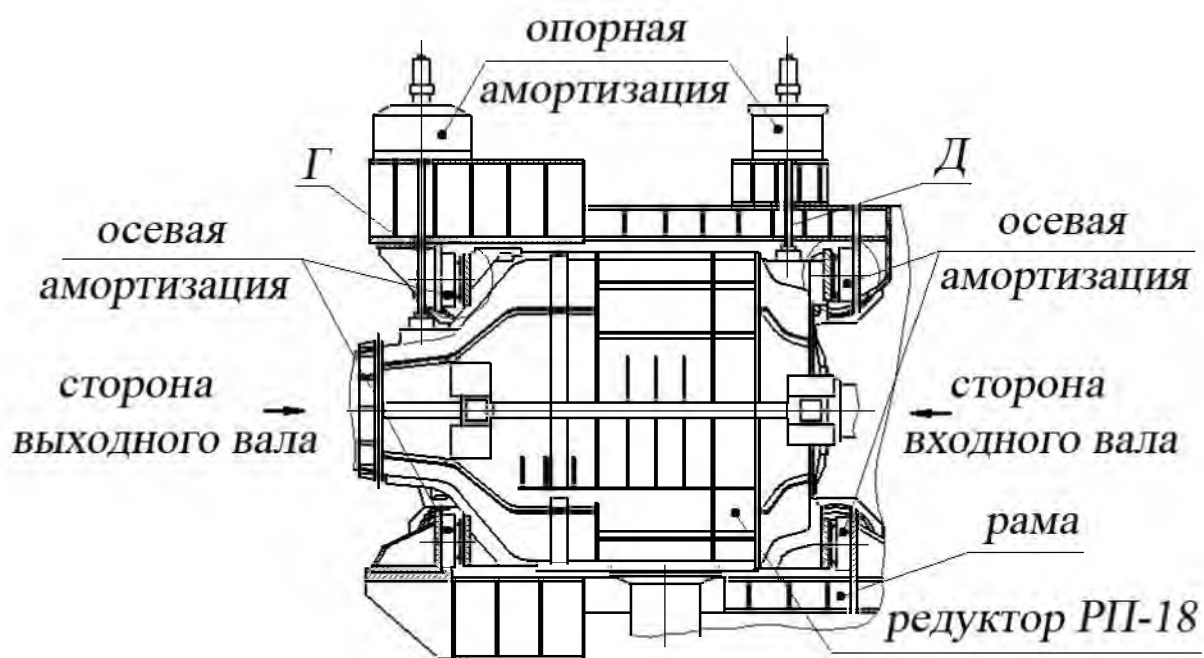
Схема крепления и амортизации редуктора (вид сбоку)
